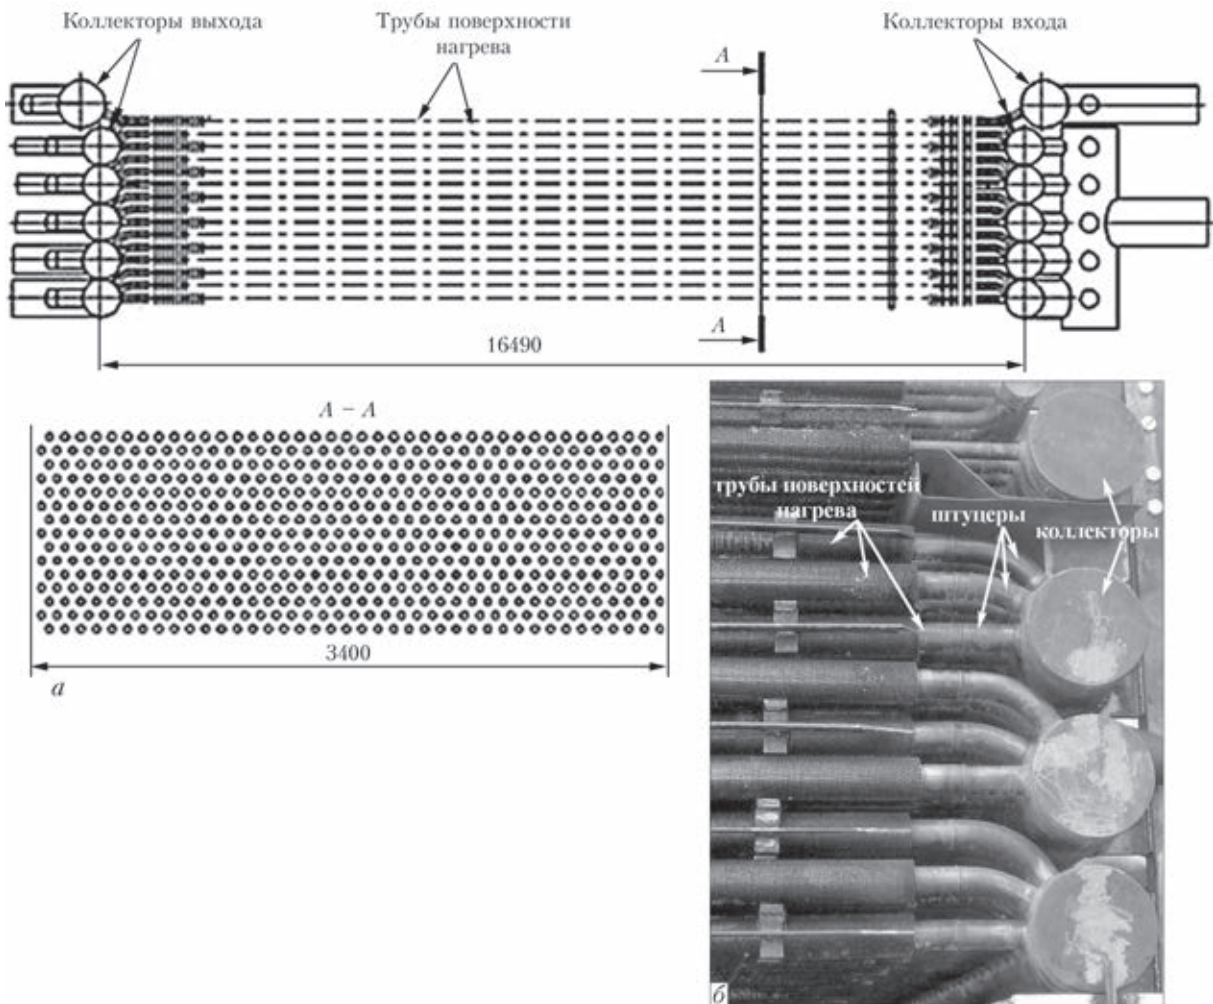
Теплообменный блок: а — схема; б — общий вид коллекторной части блока
